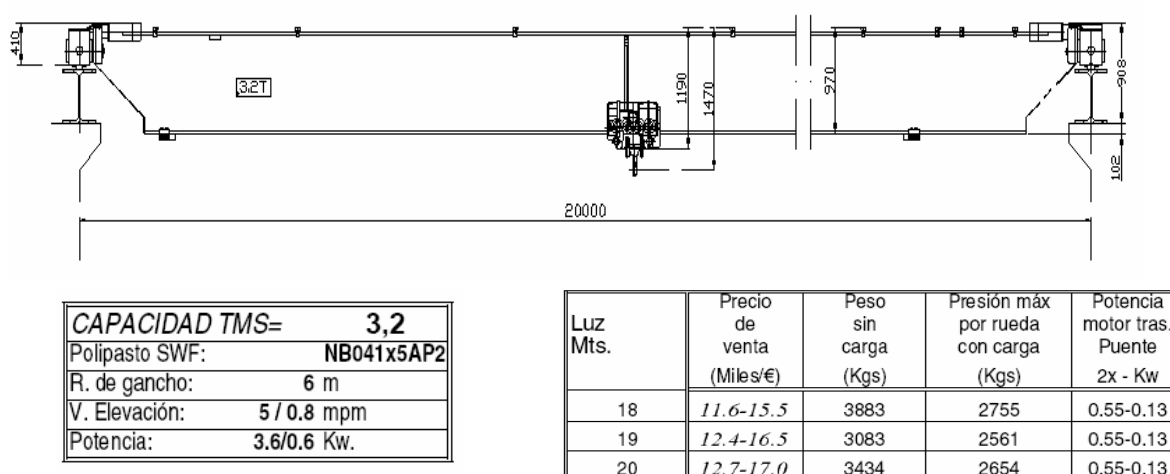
Detalle y características puente grúa monorraíl VINCA
